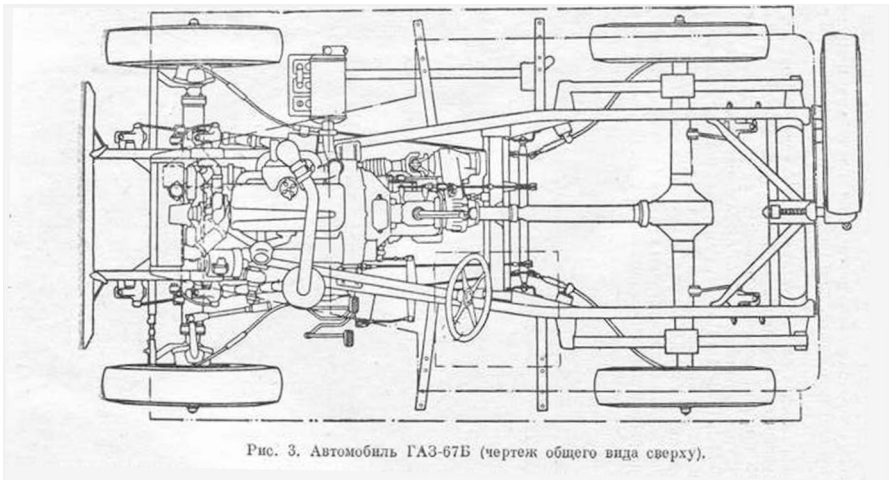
Автомобиль ГАЗ-67Б (чертеж общего вида сверху).
